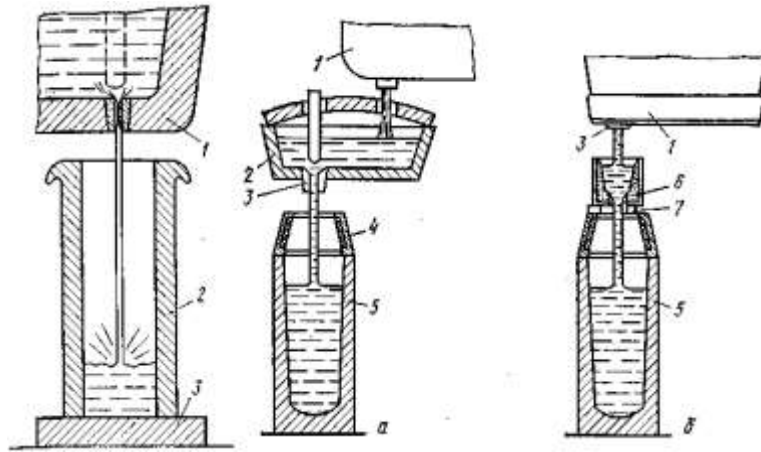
Схема розливання сталі зверху, через проміжний ківш (а)
